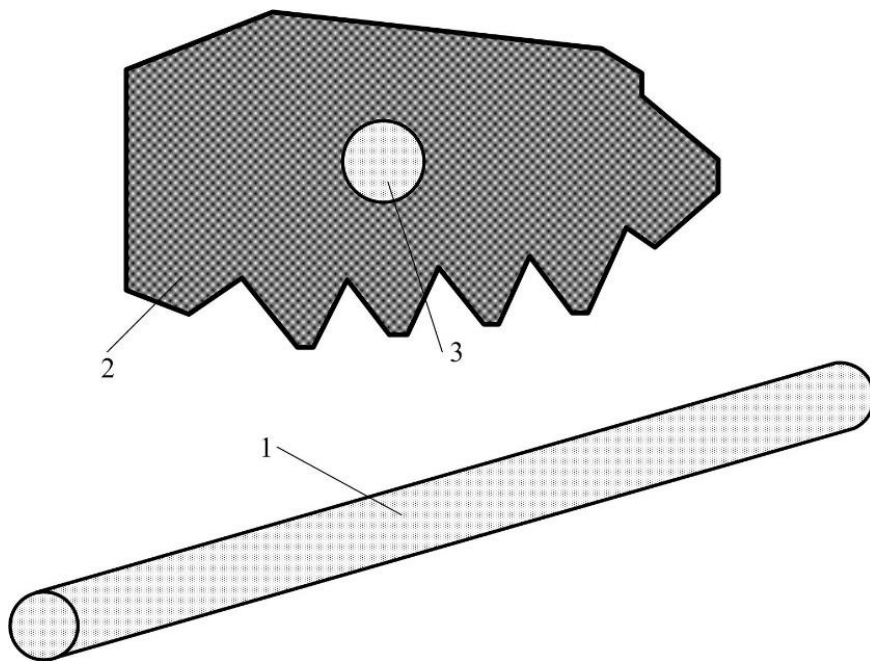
Схема конструкції ручного багатофункційного приладу для створення мінералізованої смуги: 1 – рукоятка; 2 – металеві пластина; 3 – отвір для рукоятки.
